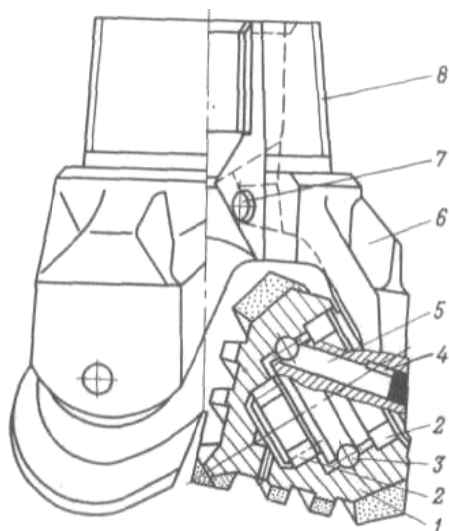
Схема конструкции трехшарошечного секционного долота с фрезерованными зубьями, наплавленным твердым сплавом: 1 – шарошка; 2 – ролики; 3 – шарик; 4, 7 – штифты; 5 – палец; 6 – лапа; 8 – базовая присоединительная резьба, расположенная на ниппельной части долота
